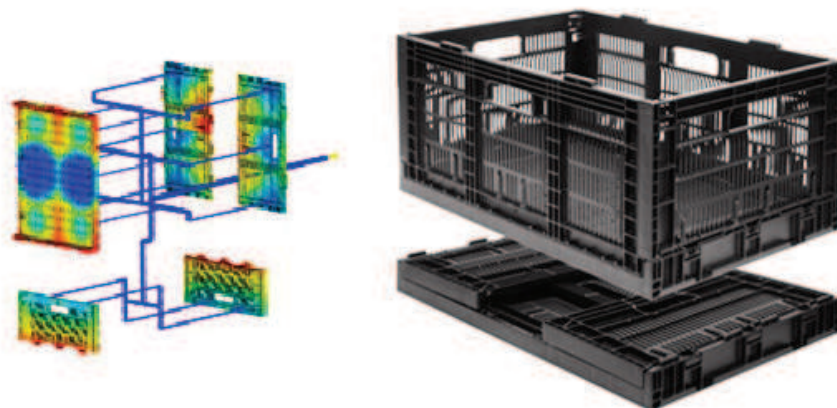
Peças diferentes a ser moldadas- *Stack mold* [12].
